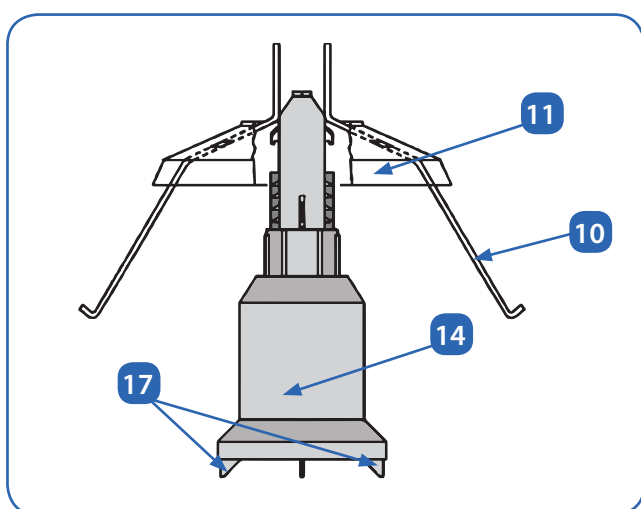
Ensamblaje de la tapa superior con el conjunto del tubo de caída.
